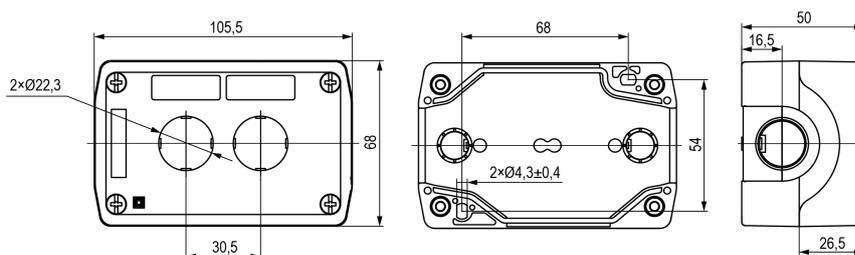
Габаритные и установочные размеры двухместного корпуса
